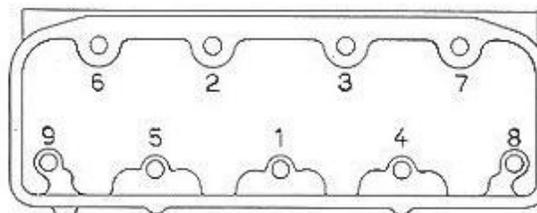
Schema der Anzugsreihenfolge der Befestigungsschrauben des Zylinderkopfes.
